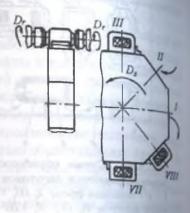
Схема обработки на барабанно-фрезерном станке двух параллельных плоскостей заготовки
